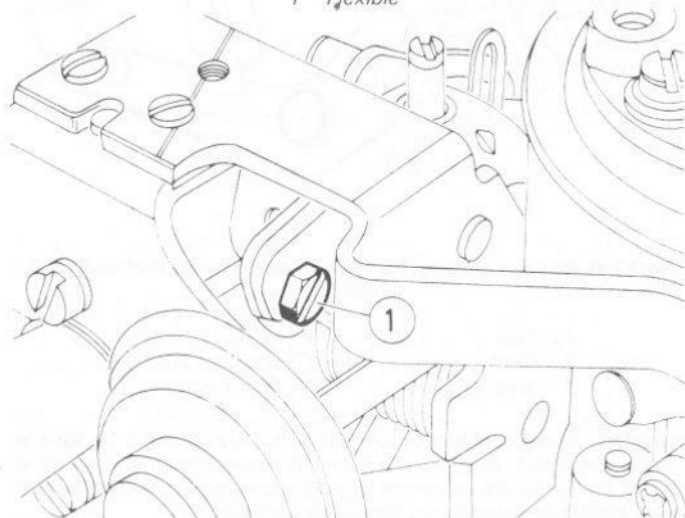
Réglage de l'OVAD - carburateur Weber 36 TLC (Sec 8)
